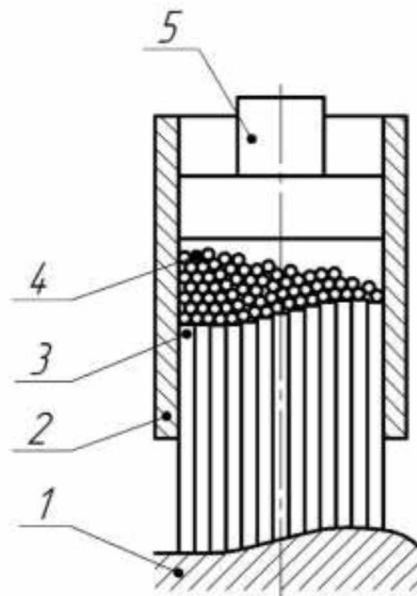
Схема багатоконтактного віброударного інструмента
